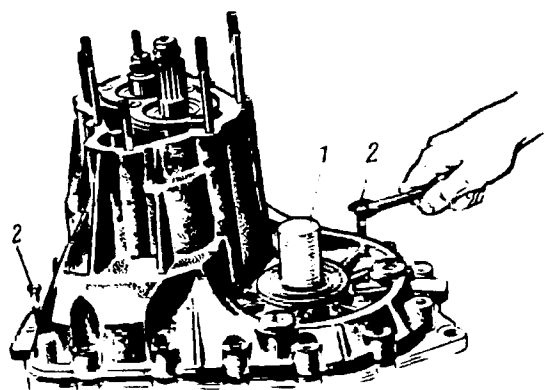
Завертывание упорных болтов в картер коробки и установка оправки в шестерню полуоси:
